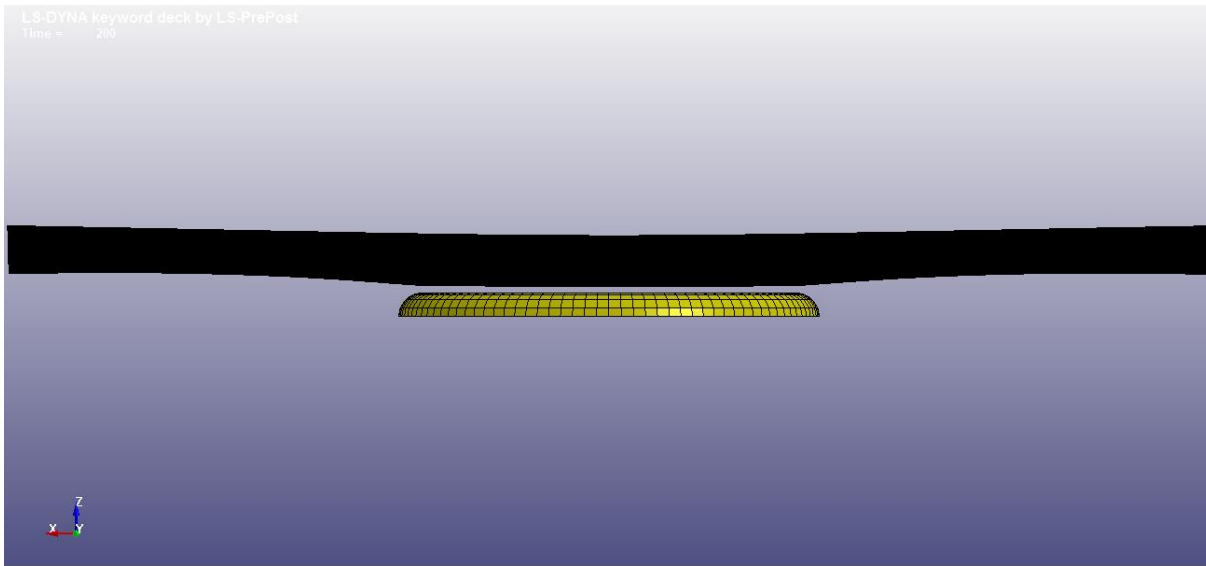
entstandene Blechgeometrie, nachdem sich die Werkzeugbacken wieder in ihrer Ausgangsposition befinden (Seitenansicht)
